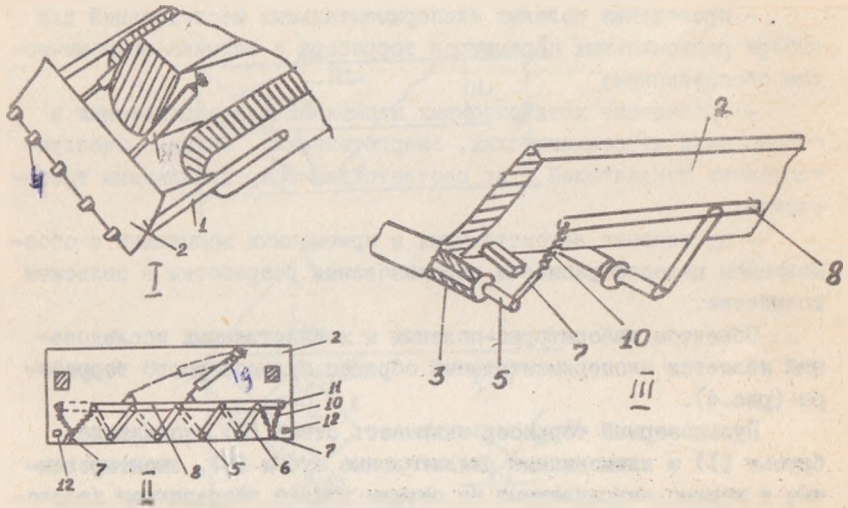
I—общий вид бульдозерного террасера; II—тыльная сторона отвала; III—схема соединения рычагов с траверсой.
